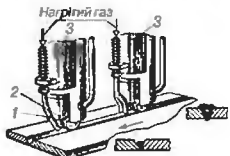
Загальний вигляд механізованого зварювального вузла і зварювальної головки:
